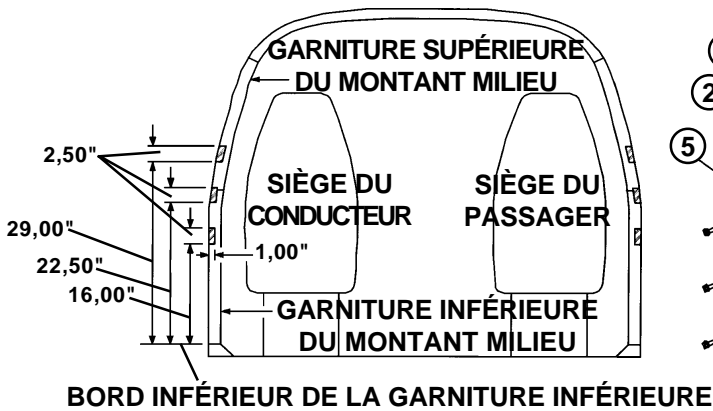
VUE DE LA FACE ARRIÈRE DES MONTANTS MILIEUX
